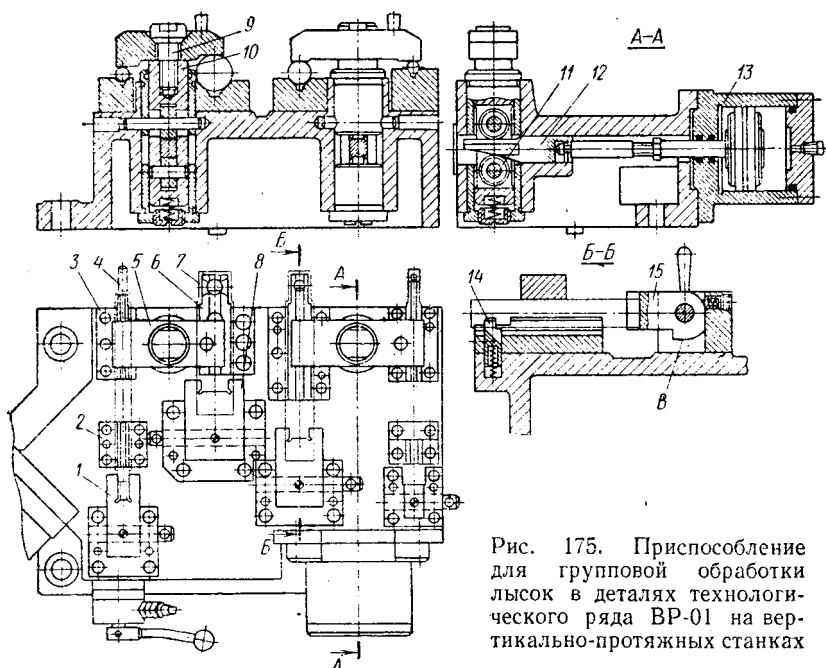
Приспособление для групповой обработки лысок цилиндрических деталей технологического ряда ВР-01 на вертикально-протяжных станках
